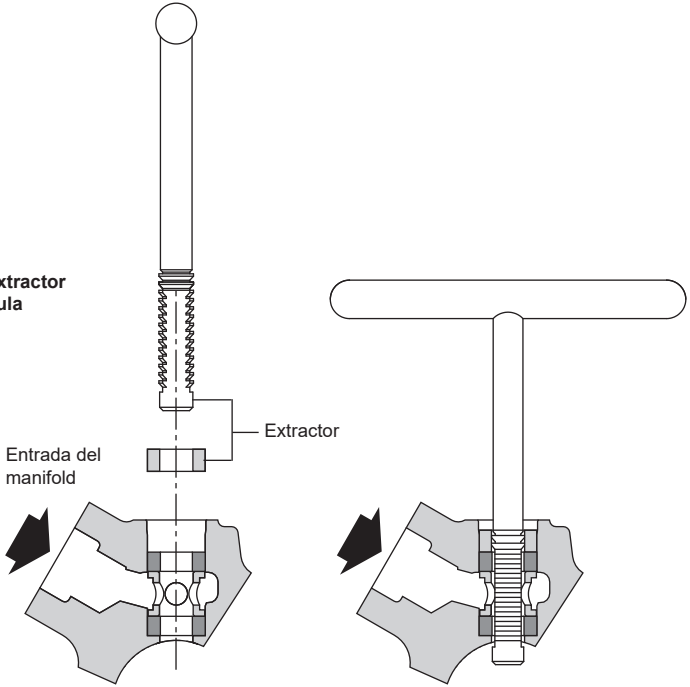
Vista que muestra el extractor de partes internas de la válvula
